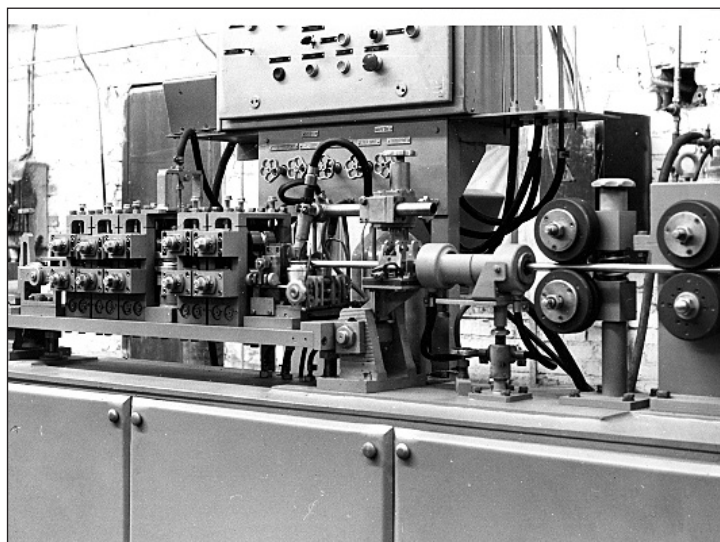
Формовка ленты в трубную заготовку и сварка кромок
